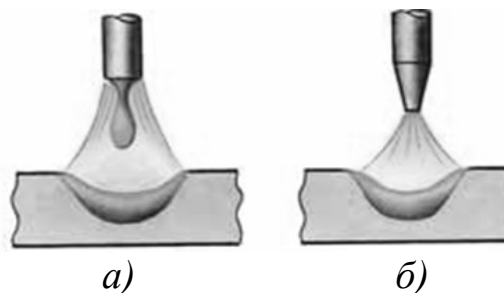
Схема сварки плавящимся электродом (а) и сварки неплавящимся электродом (б)
